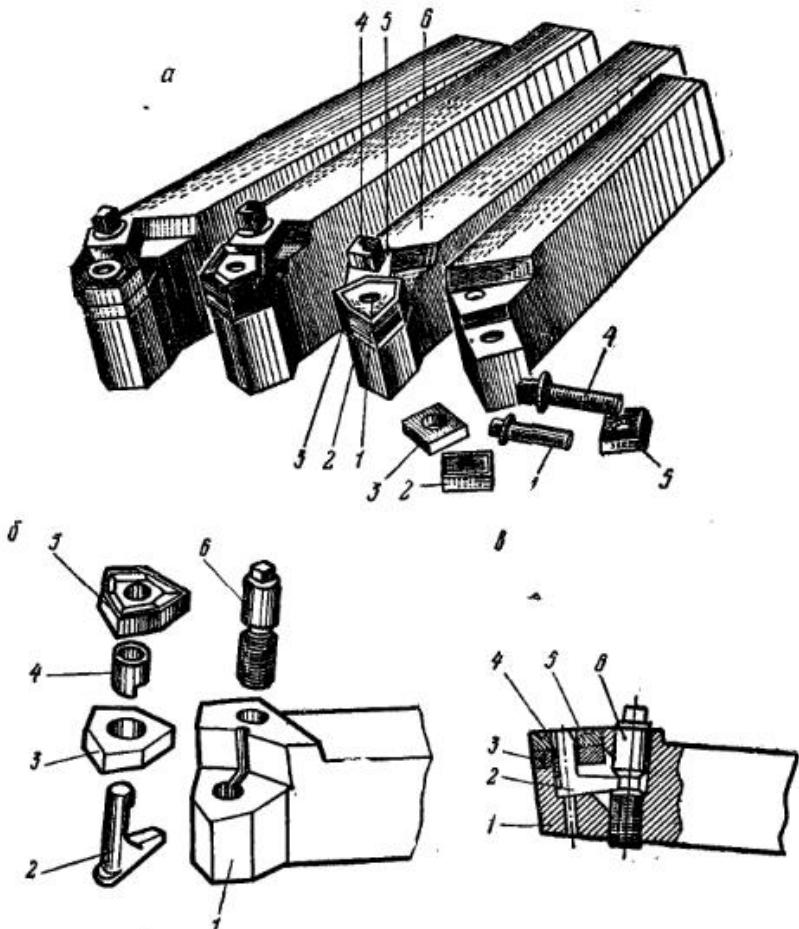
Конструкция резцов с механическим креплением многогранных пластинок твердого сплава:
